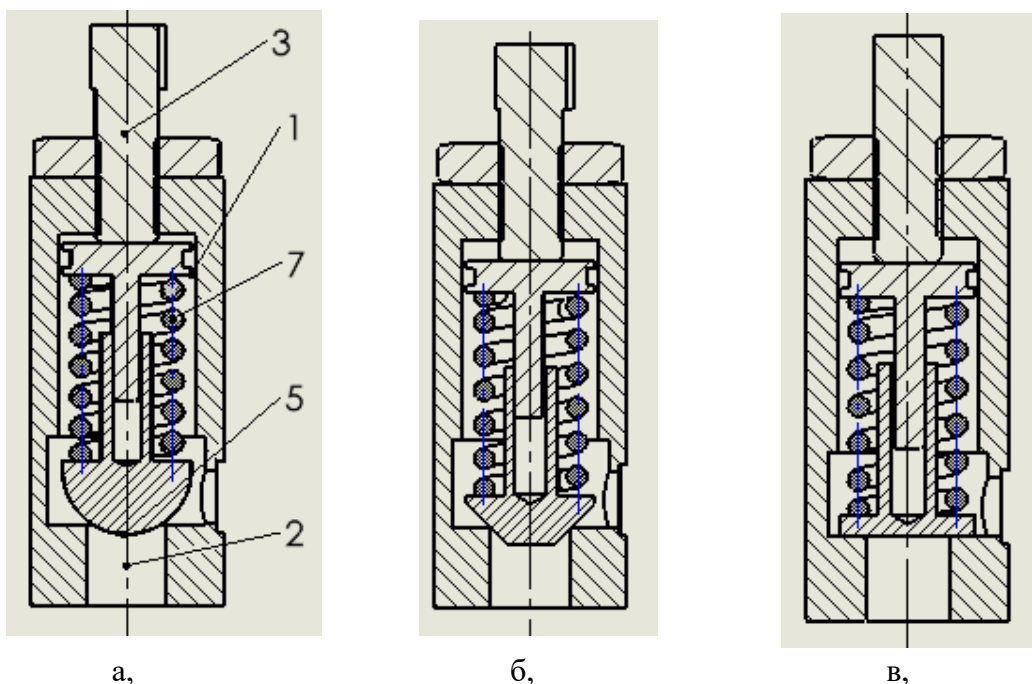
Принципиальные схемы предохранительных клапанов с запорно-регулирующими элементами: а - с шариковым; б - с коническим; в - с тарельчатым (пластинчатым)
